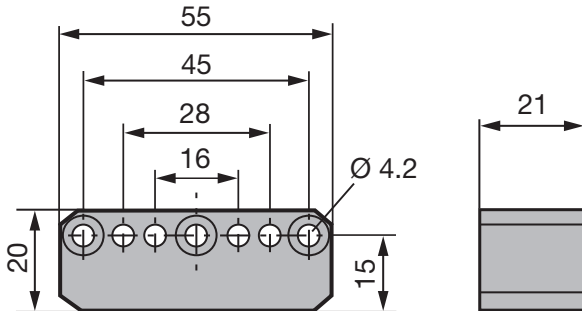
Medidas de montaje del sensor de posición BTL5-P-5500-2
